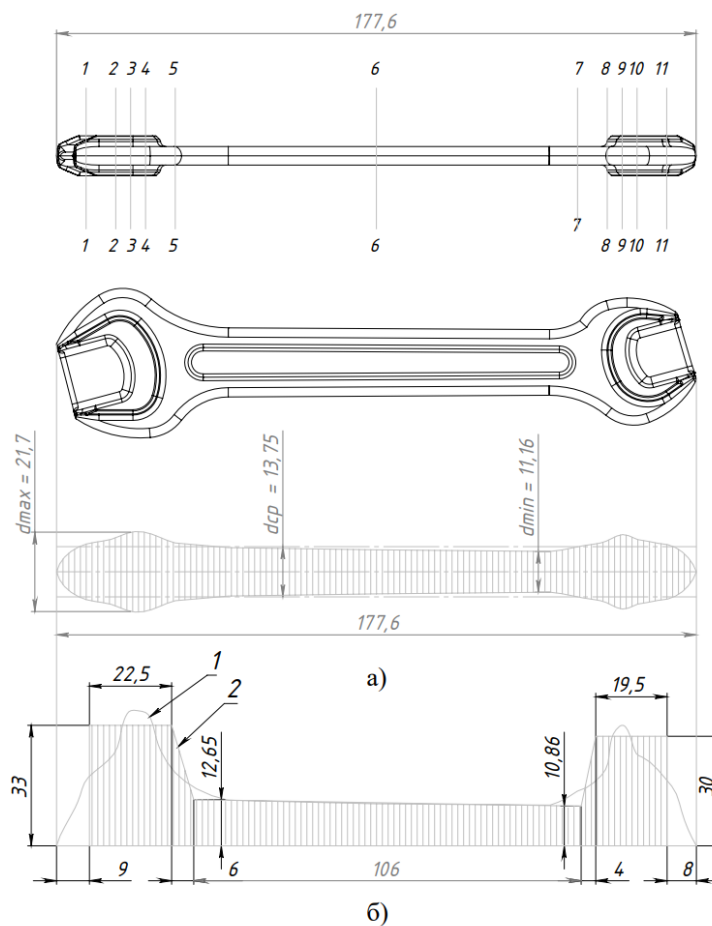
Эпюра диаметров и сечений: а – развертка поковки рожкового гаечного ключа и расчетная заготовка (эпюра диаметров); б – эпюра поперечных сечений (1 – поковки, 2 – вальцованной заготовки)
